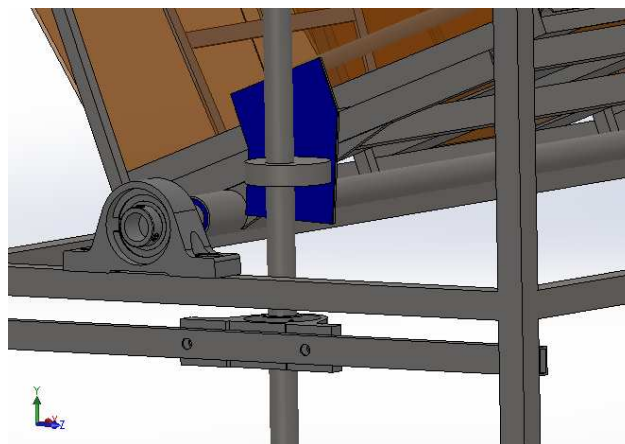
Pormenor do Shaking, com o batente a proteger a cames
